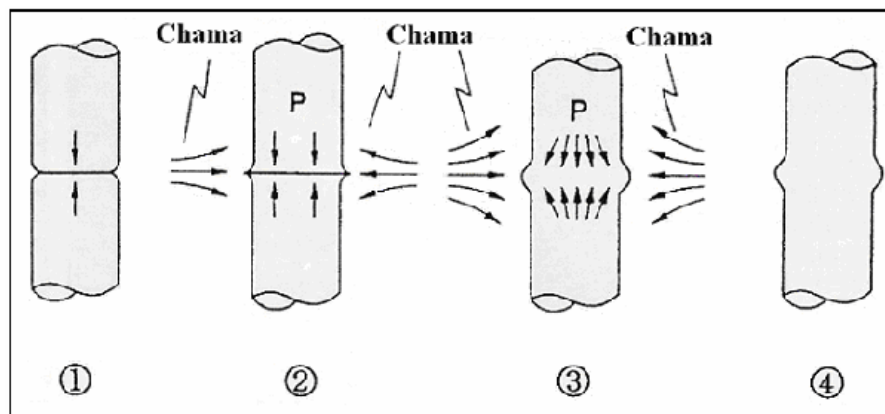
Etapas da soldagem por caldeamento com chama [3].
